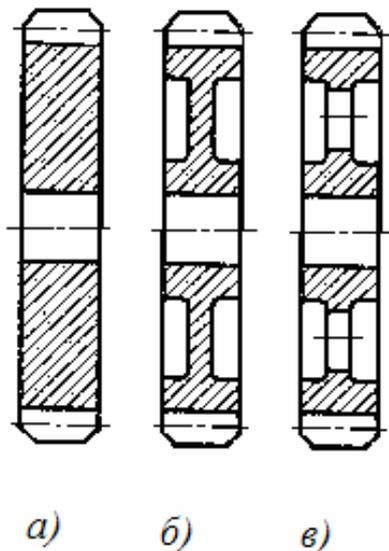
Облегчение дисковой шестерни (а) за счёт удаления металла глухими (б) и сквозными (в) выборками
